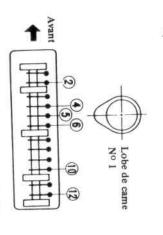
Ordre de réglage du jeu des soupapes ET 436
